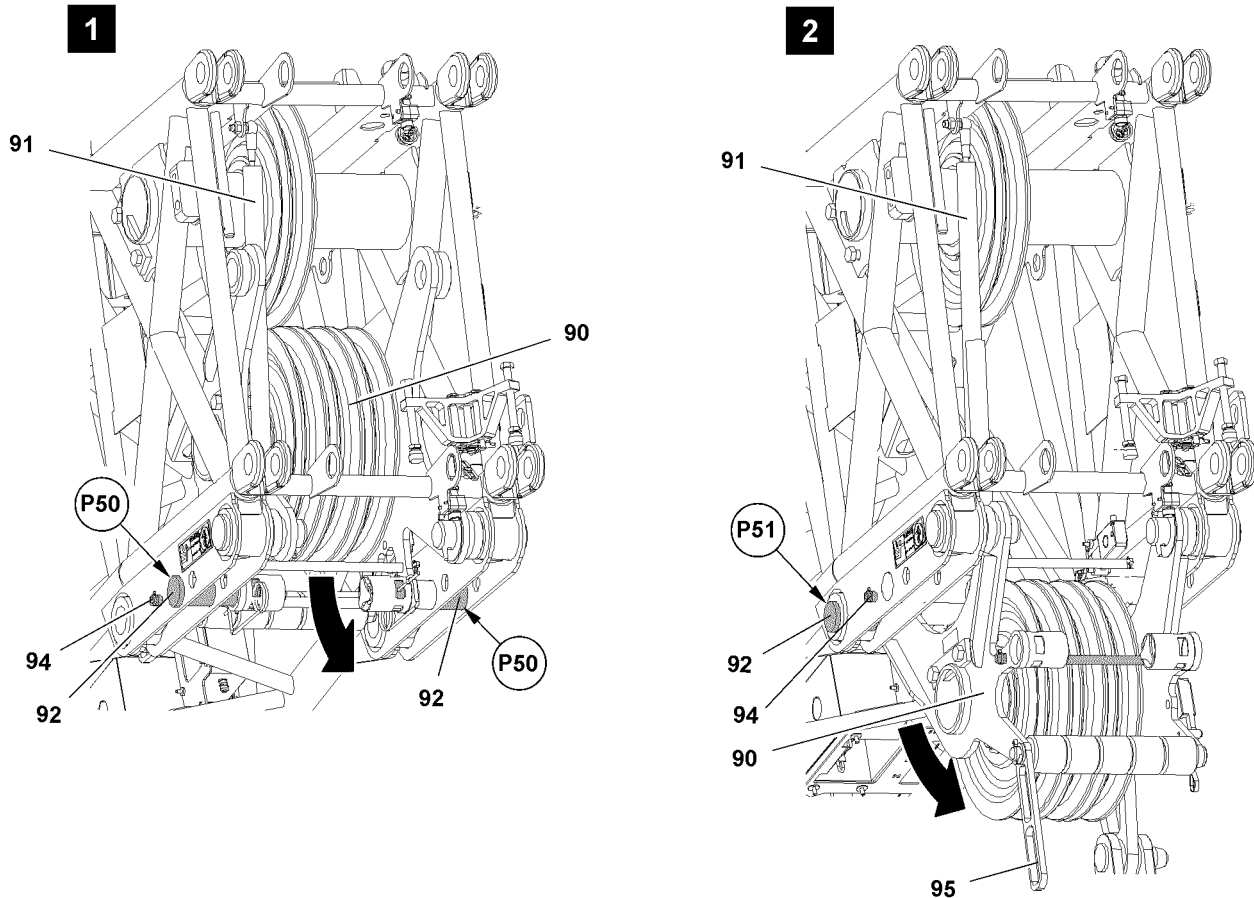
Pinar o conjunto de roldanas em posição de operação
